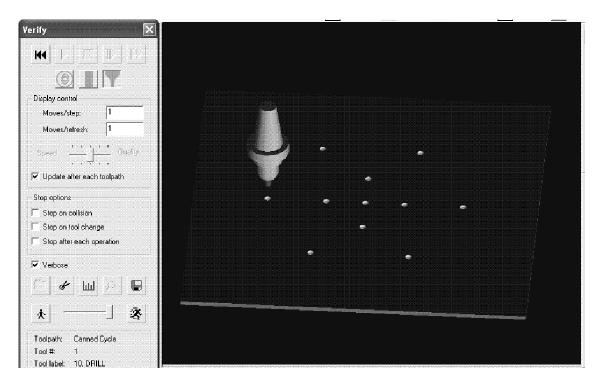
Barrenado de la pieza con Drill Point Selection
